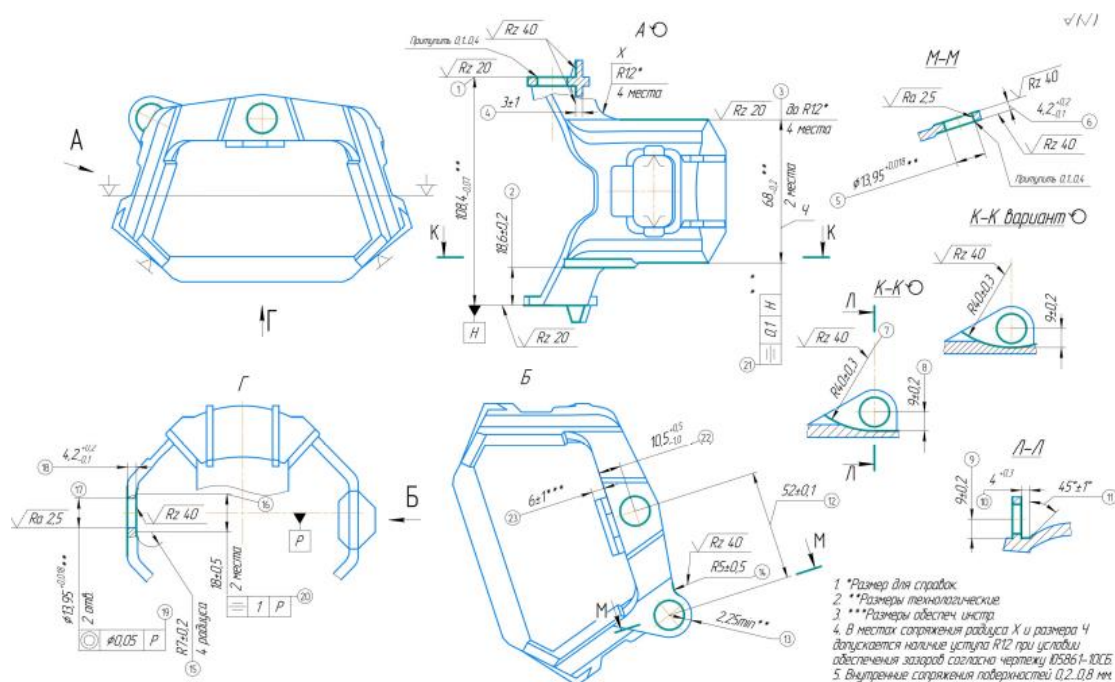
Эскиз к операции 035 – Фрезерная с ЧПУ
